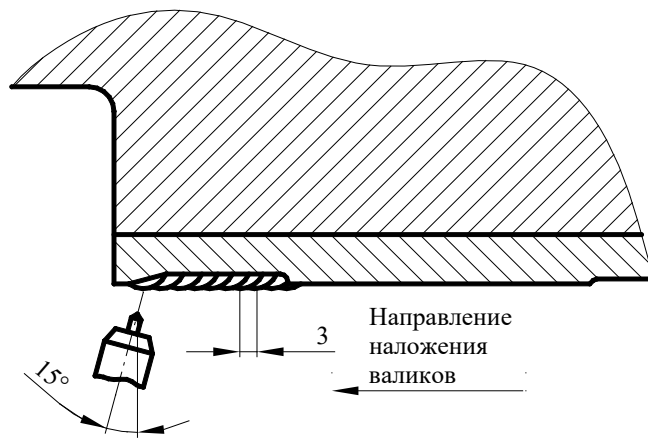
Підготовка ущільнюючої поверхні кришки ВБ під наплавлення
